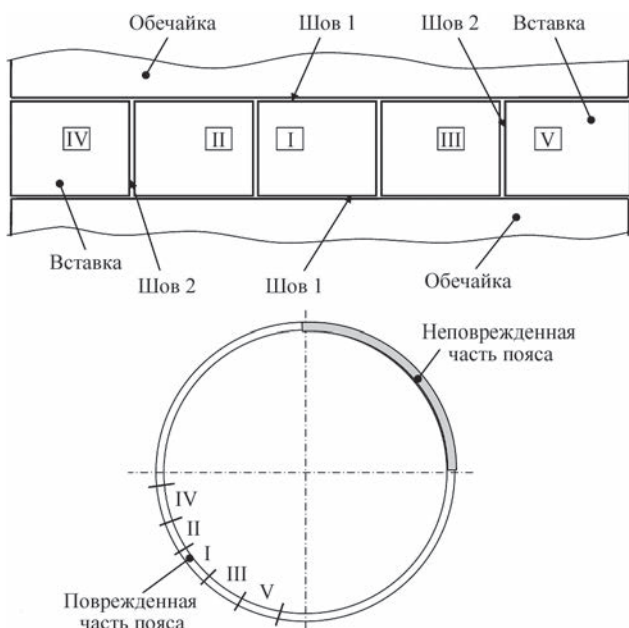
Очередность сварки вставок при ремонте регенератора Р-202
